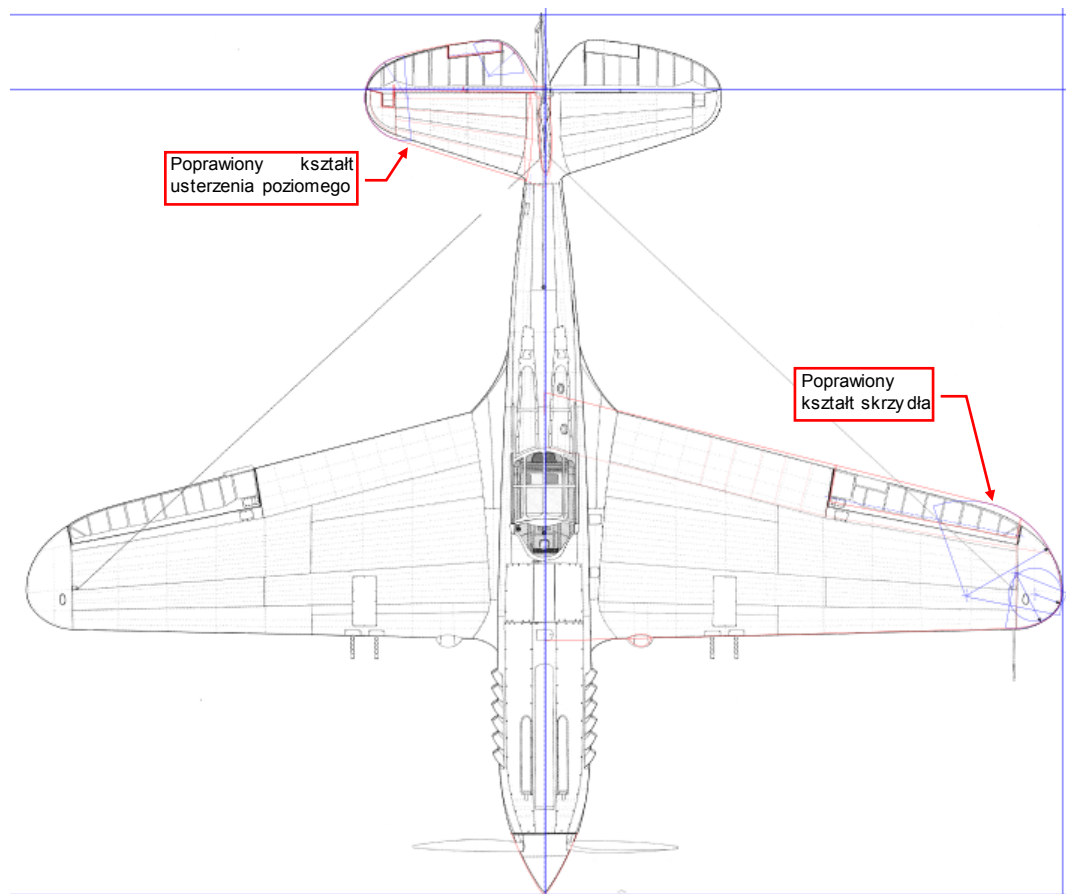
przedstawia korekty naniesione na plan usterzenia poziomego (statecznika i steru).
